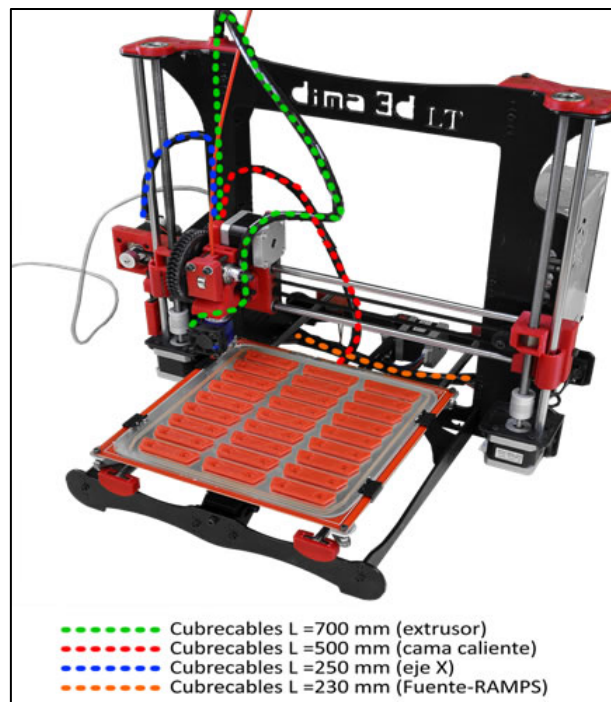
Colocación de los cubrecables. Fuente: BPMSat. Ref: [41]
